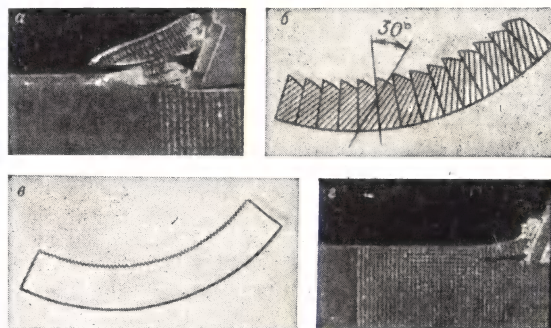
Виды стружки: а — элементарная; б — скальвания; в — сливная; г — надлома.
